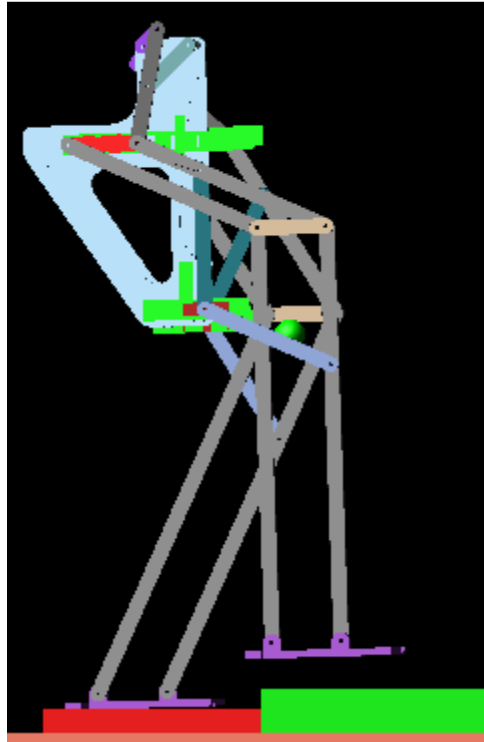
Elevación y alargamiento de la zancada del pie derecho
